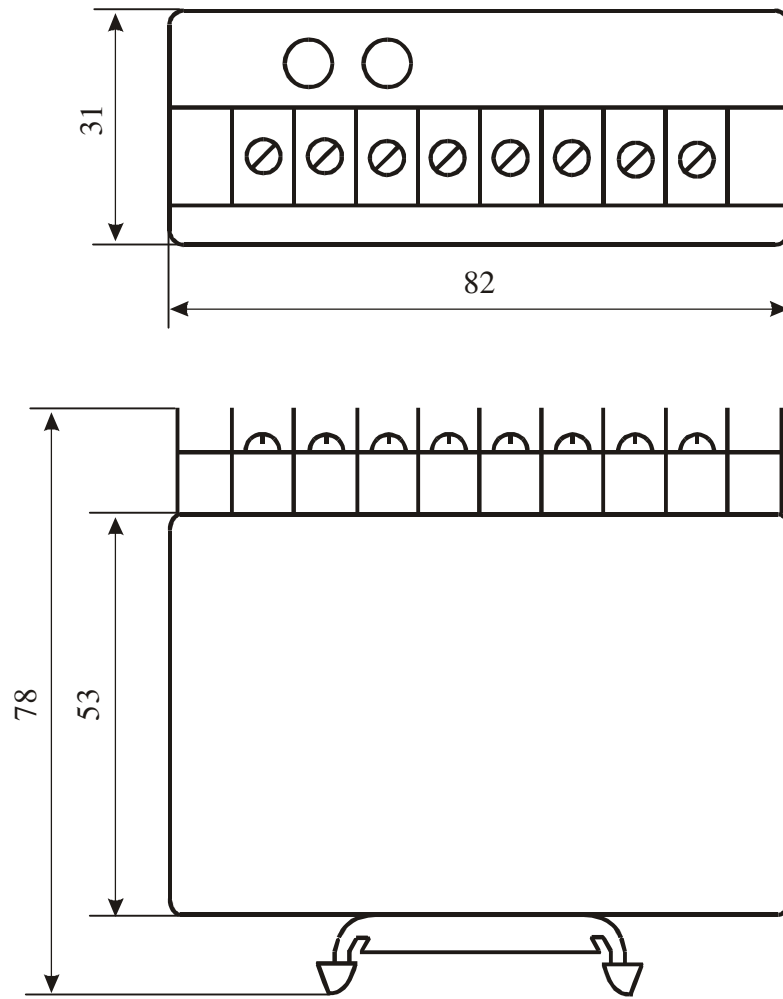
Габаритный чертёж ИП-40030-2-0-В4, ИП-40030-2-0-С4,
